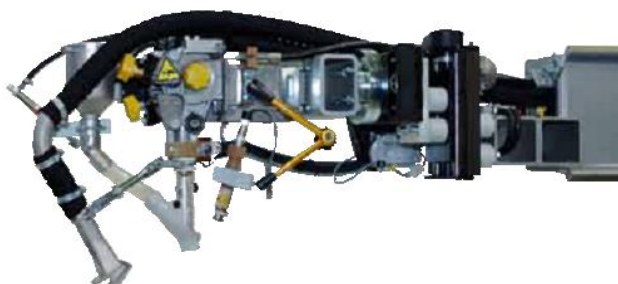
Зварювальна головка ESAB A6S Compact 500
